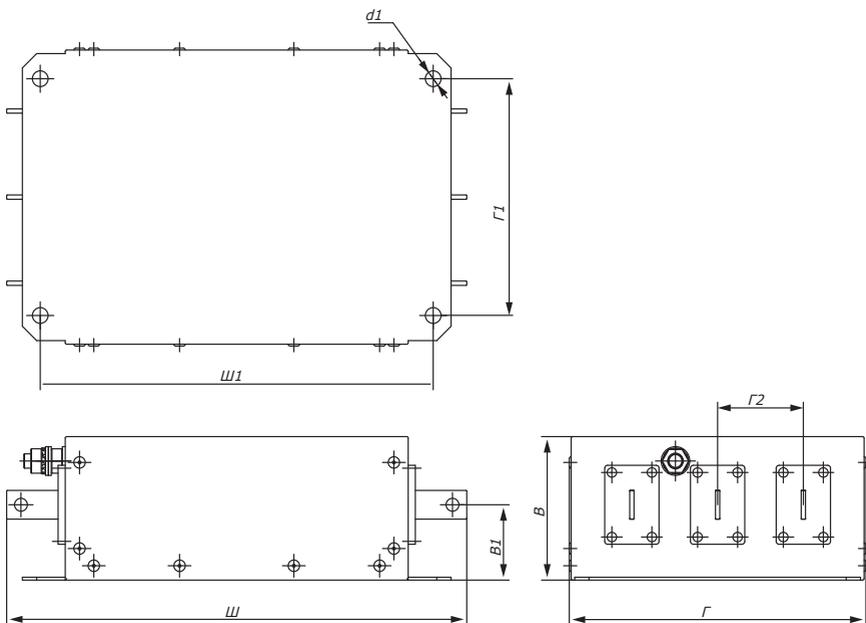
Габаритные и установочные размеры IFE-37K-76-380
